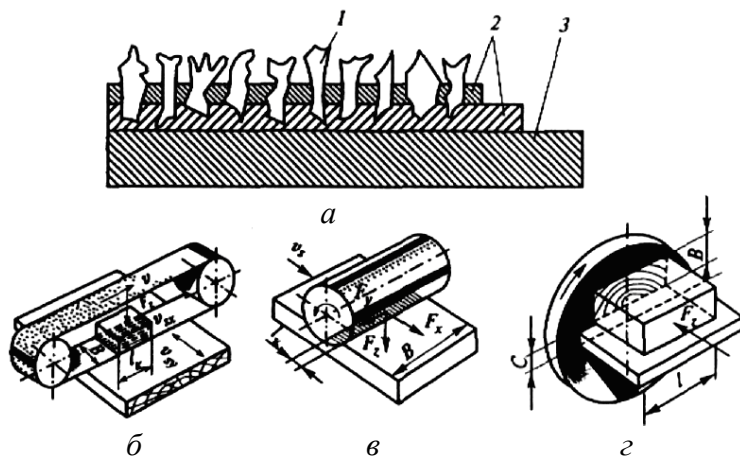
Схема сечения шлифовальной шкурки (а) и схемы ленточного (б), цилиндрического (в), дискового шлифования (z)
